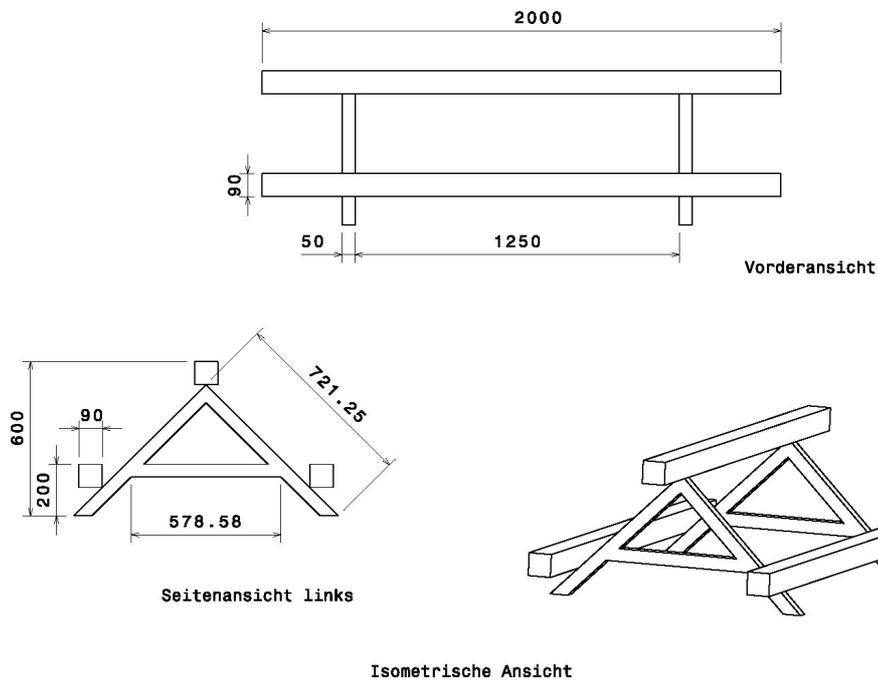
Bauplan einer Sitzstangenkombination (mit Maßangaben in mm)
